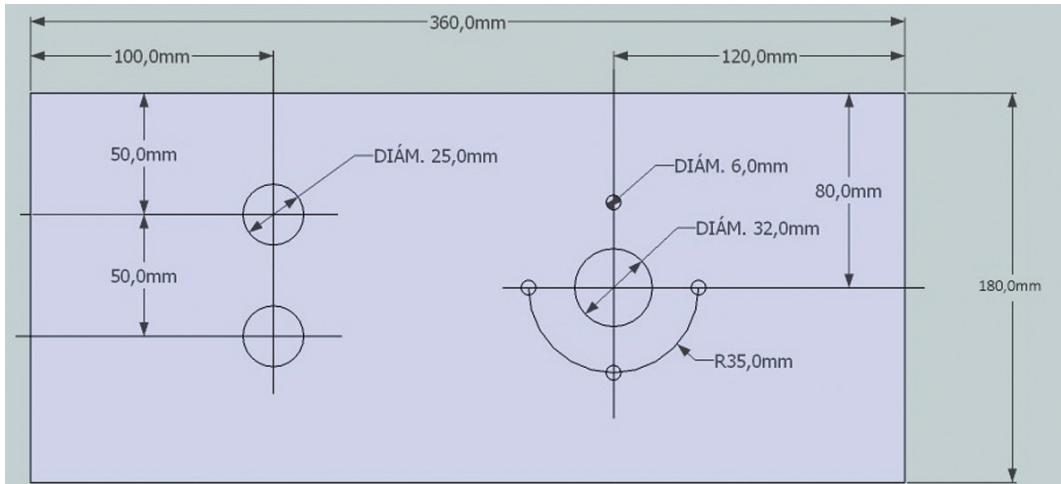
| Plantilla con las medidas de la parte superior de la consola.
